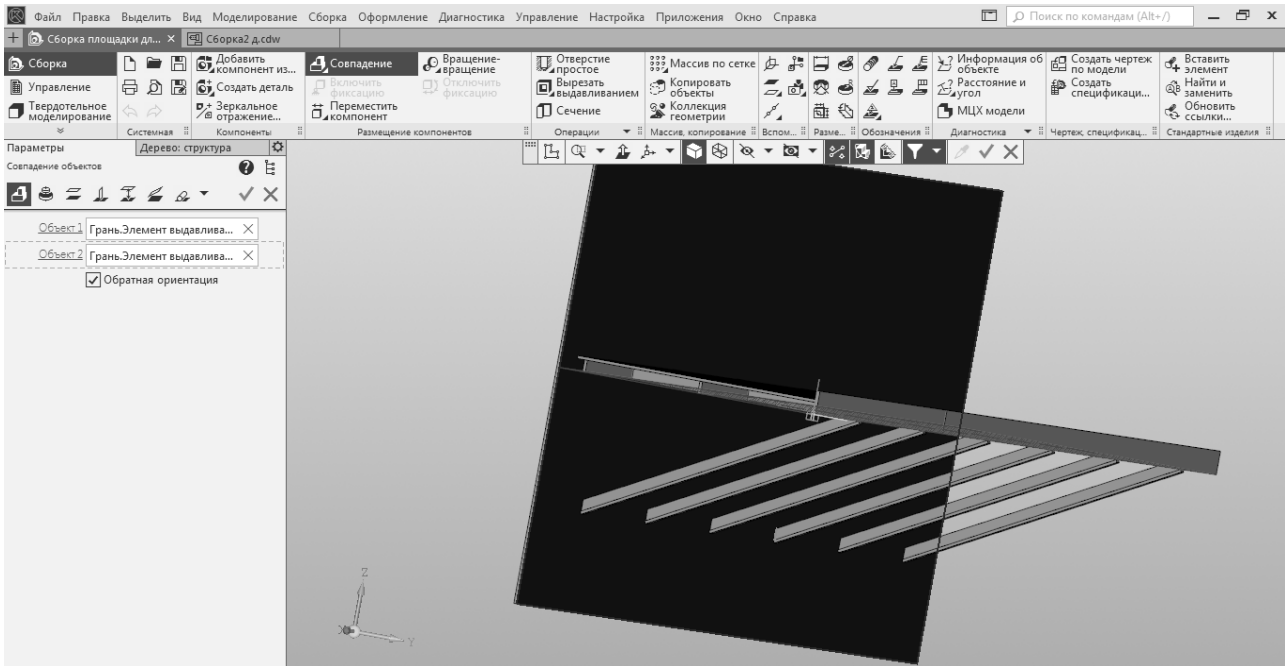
Крепление площадки с помощью дополнительных тавровых балок к листу
